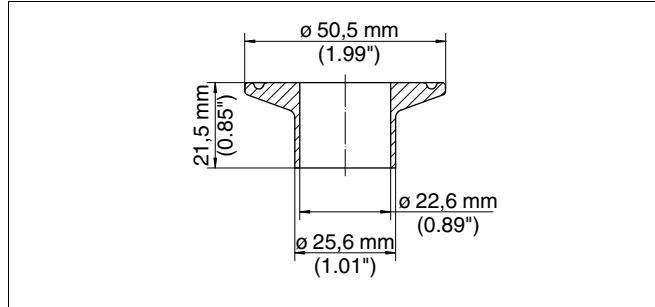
Mesure raccord à souder Clamp 1" PN16 DIN 32676, ISO 2852/316L
